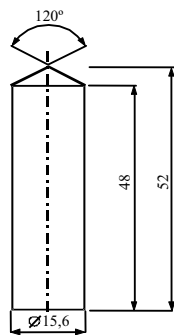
Pistón cilíndrico de bronce, dimensiones en mm.
